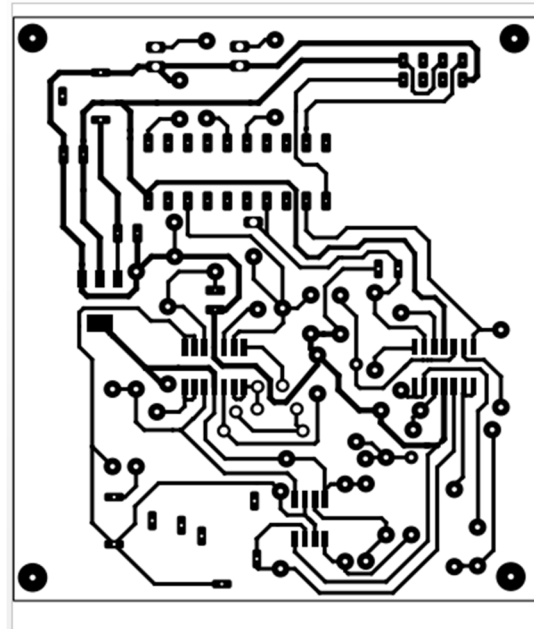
PCB Bottom-View. Fuente: Autor.
